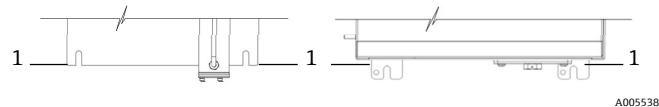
Расположение выступов с прорезями (1) для установки анализатора J22 на панель (слева) или в корпус (справа)
